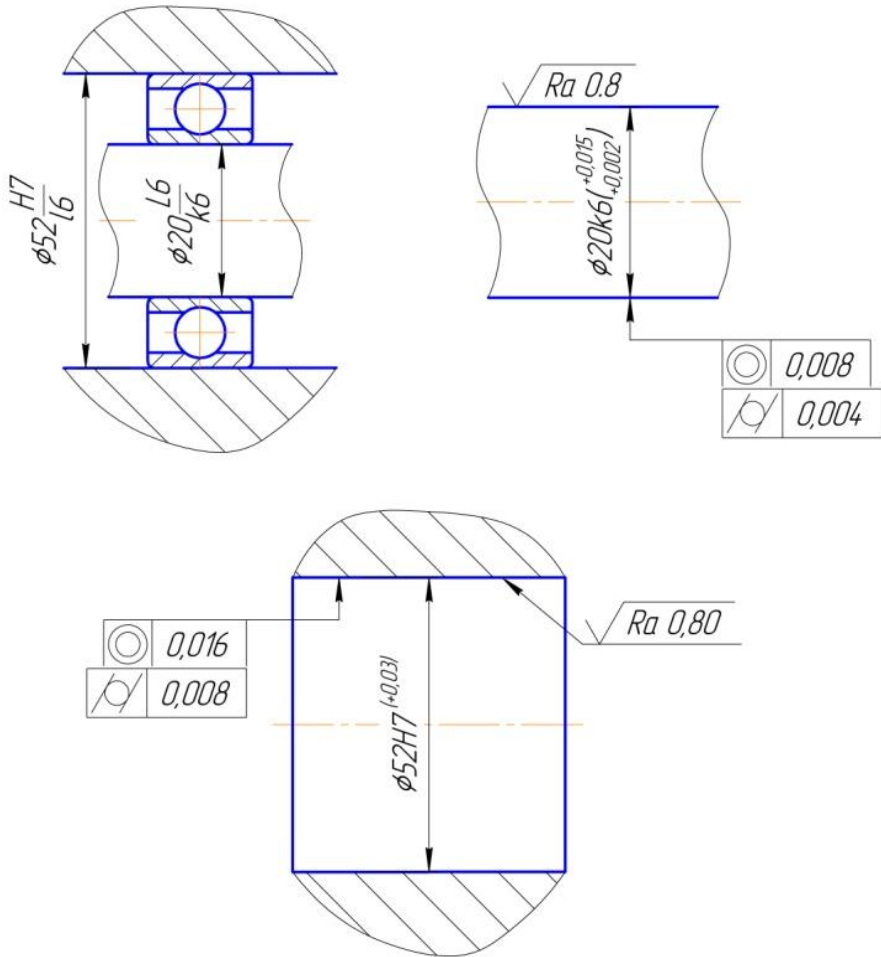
Ескізи підшипникового вузла, корпусу і вала
